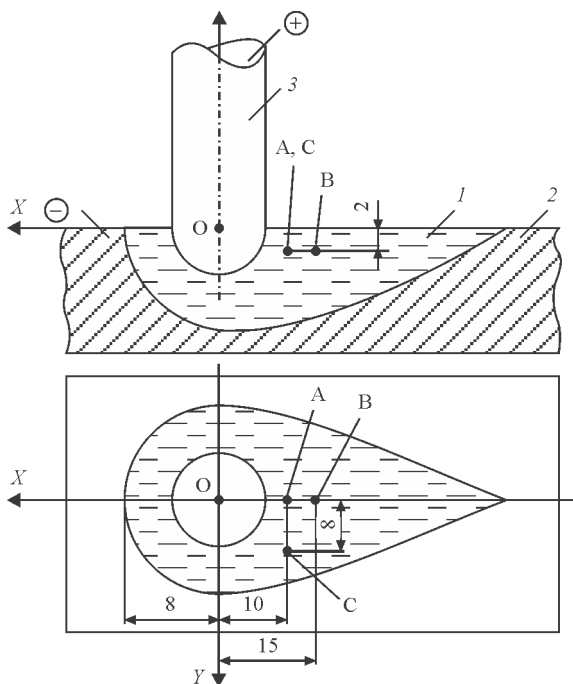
Схема модельної ванни для вивчення в ній руху рідкого металу: 1 – розплавлений припій – ванна; 2 – пластинка-виріб; 3 – штир-електрод
